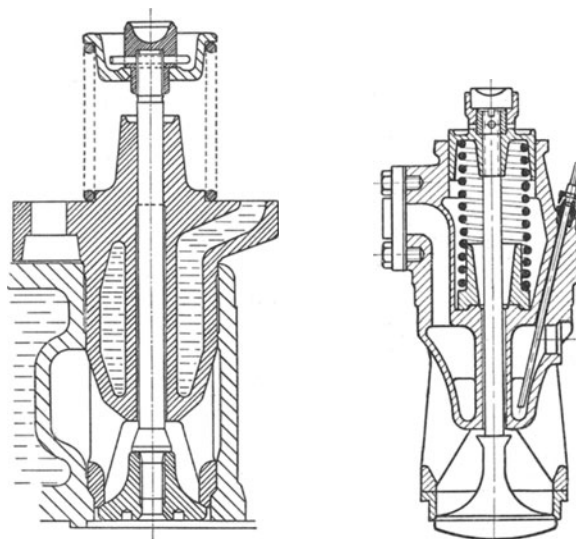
44. Auspuffventile mit gekühlten Gehäusen.
